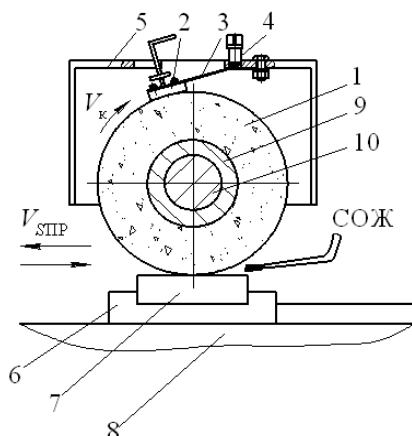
Установка для механической очистки ШК упругозакрепленной абразивной лентой: 1 – ШК; 2 – инструмент для очистки; 3 – упругая пластина; 4 – винт; 5 – кожух; 6 – динамометр УДМ-100; 7 – заготовка; 8 – стол станка; 9 – планшайба; 10 – шпиндель
